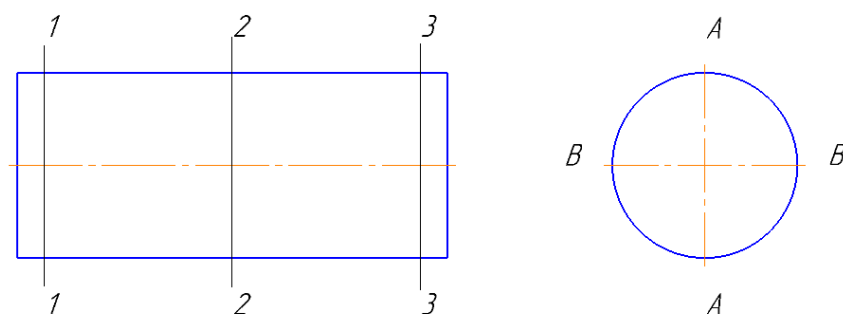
Схема контроля гладкой цилиндрической поверхности
